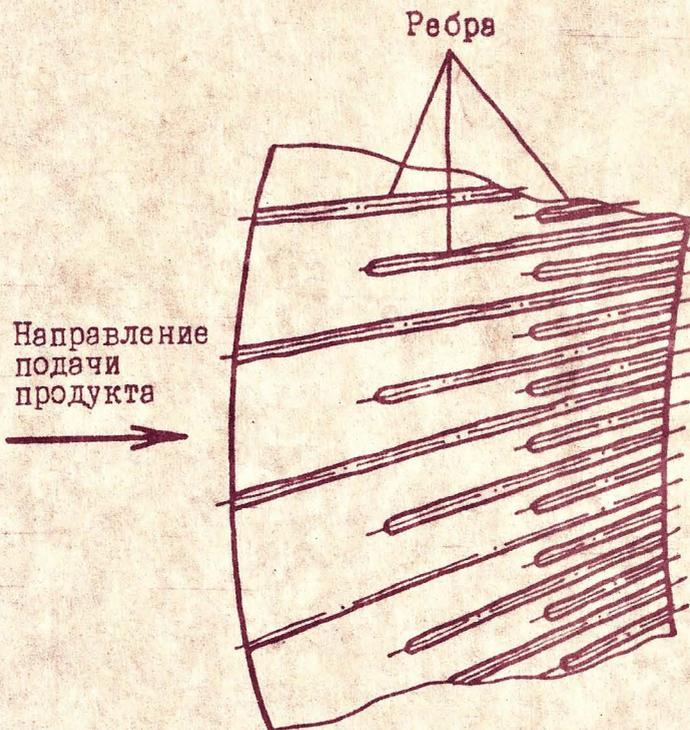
Развертка рабочей части корпуса со спиральными ребрами
